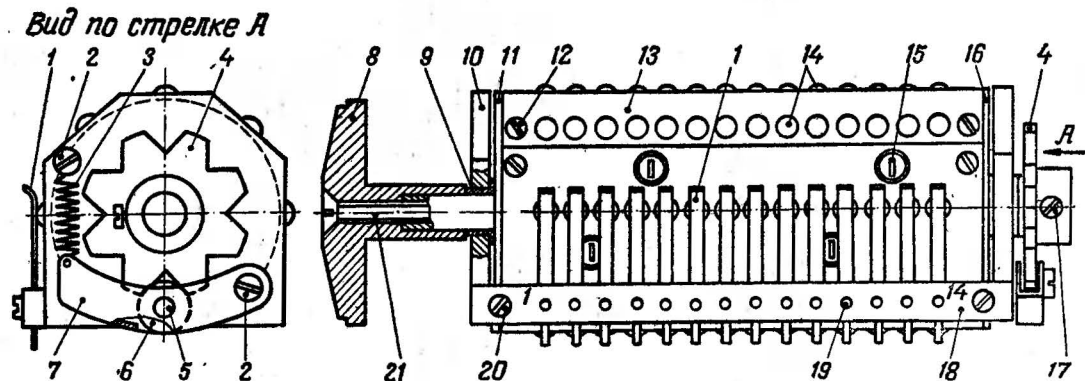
Переключатель диапазонов в сборе: 1 — контакт неподвижный, 14 шт., закрепить на дет. 18 заклепками 19; 2 — винт специальный, 2 шт.; 3 — пружина, проволока стальная класса II диаметром 0,3 мм, 15—20 витков на оправке диаметром 2 мм; 4 — звездочка; 5 — штифт, Ст.20, расклепать в дет. 7; 6 — ролик; 7 — коромысло; 8 — ручка, Д16-Т; 9 — втулка, 2 шт., запрессовать в дет. 10; 10 — корпус; 11 — полуось большая; 12 — винт М1,7×6, 16 шт.; 13 — планки, 4 шт.; 14 — контакты подвижные, 112 шт., запрессовать в дет. 13; 15 — каркас катушки; 16 — полуось малая; 17 — винт М2,5×4; 18 — планка; 19 — заклепка  $\varnothing 1 \times 3,5$  мм, 14 шт.; 20 — винт М2×6, 2 шт.; 21 — винт М3×20
